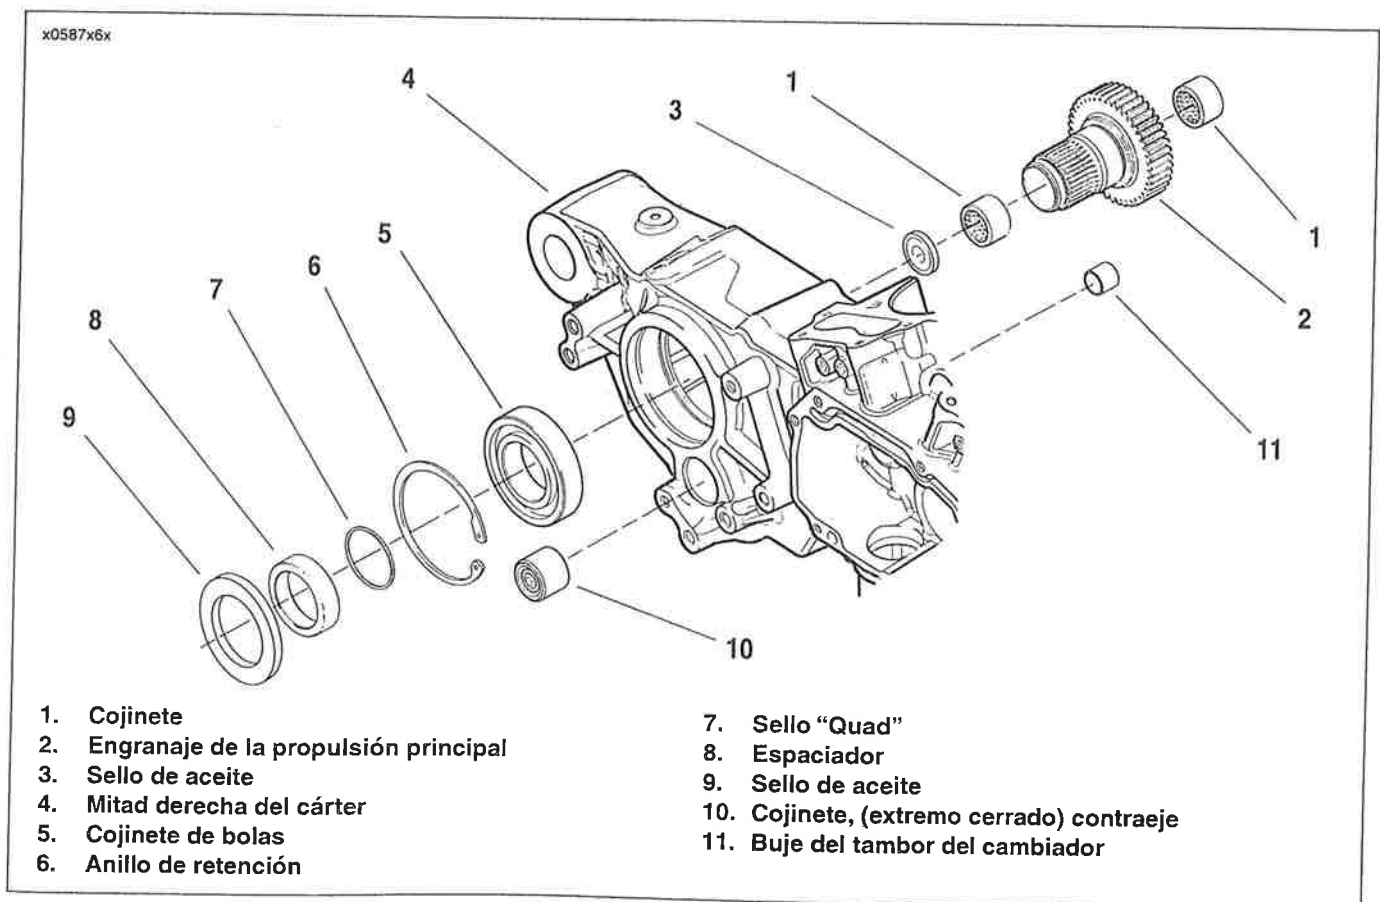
Lubricación de los cojinetes de aguja del engranaje de la propulsión principal
